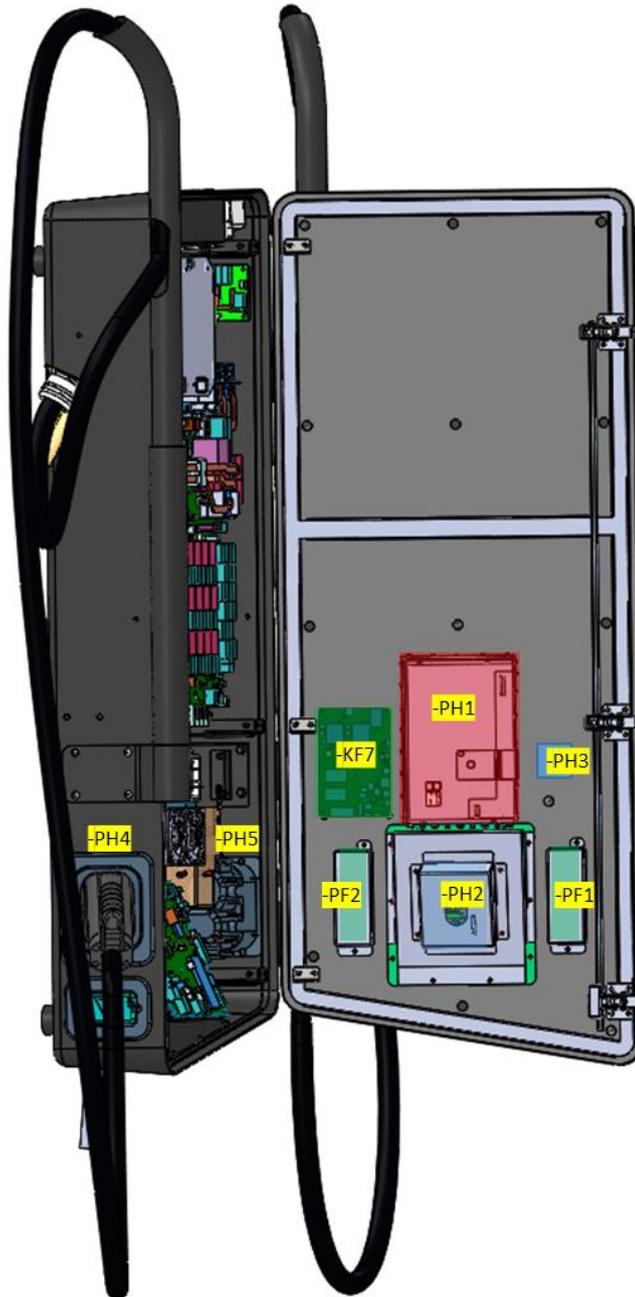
Innenansicht HYC_50 (Front Rückseite mit 2x DC-Ladekabeln)
